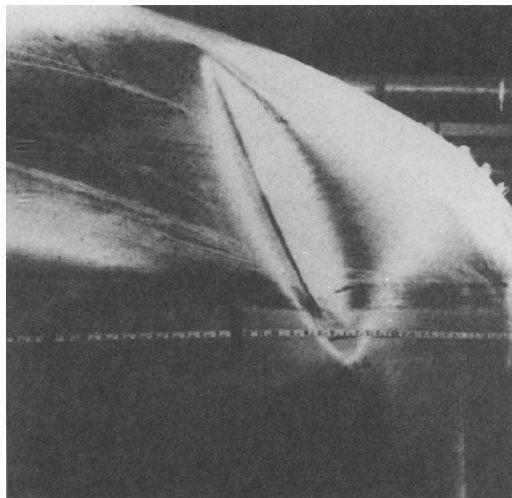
Fonte: GALLETLY 1982 [8] Detalhe de um vaso de pressão com tampo torisférico que sofreu flambagem.
